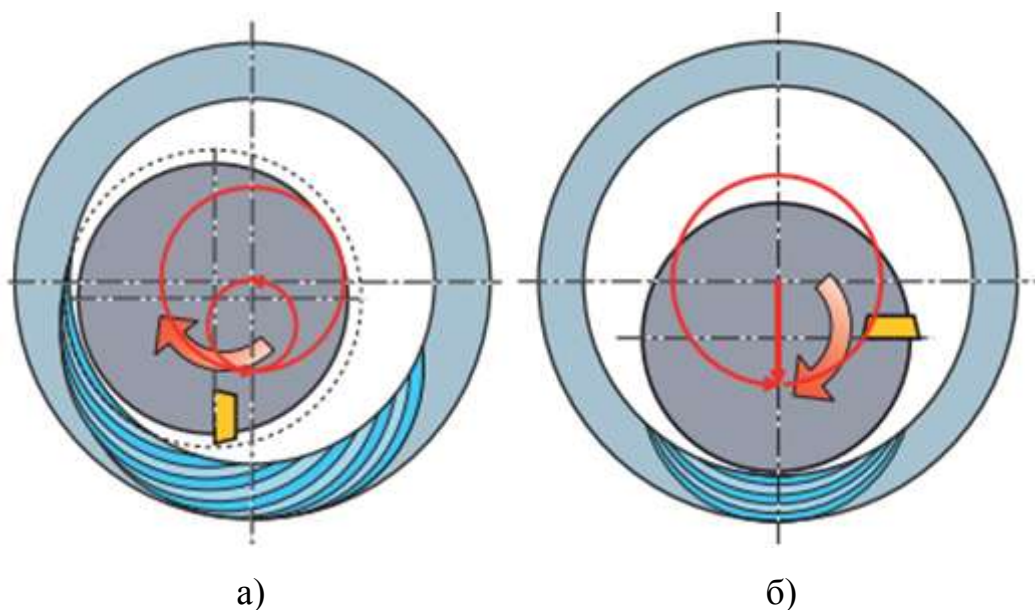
Подвод инструмента: а) тангенциальный подвод по дуге;
